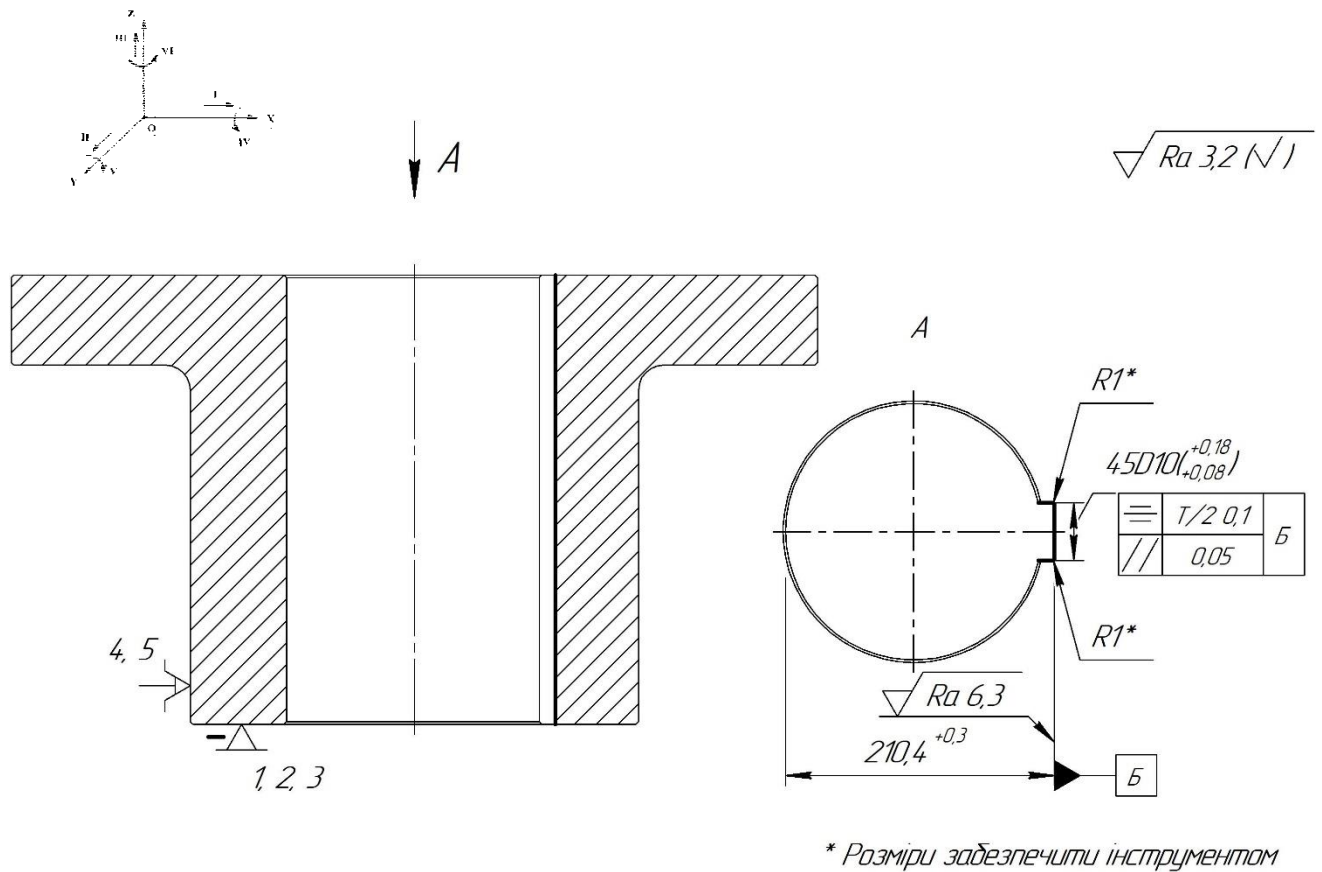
Схема базування й закріплення заготовки на операції довбальній 035
